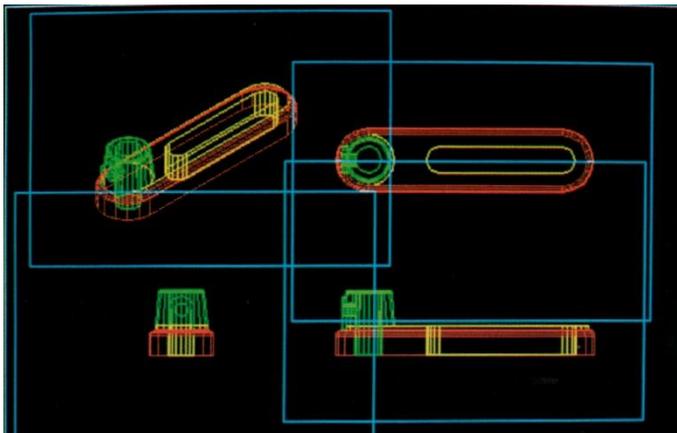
AutoCad* 10 (Fonte: An AutoCAD Workbook⁹⁹)
